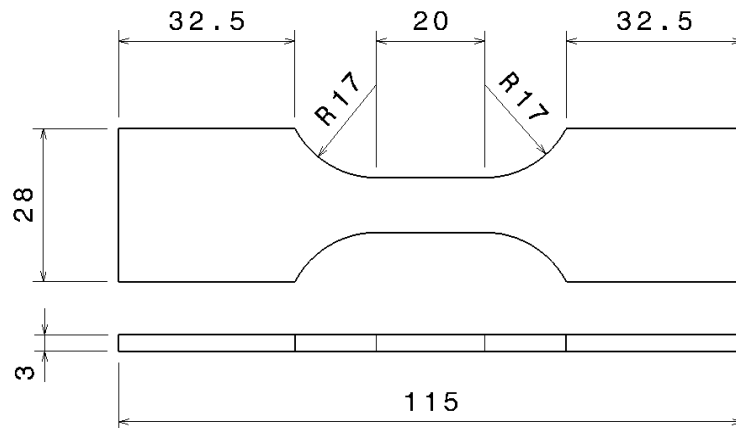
Géométrie et dimensions de l'éprouvette utilisée pour le test de moulage
